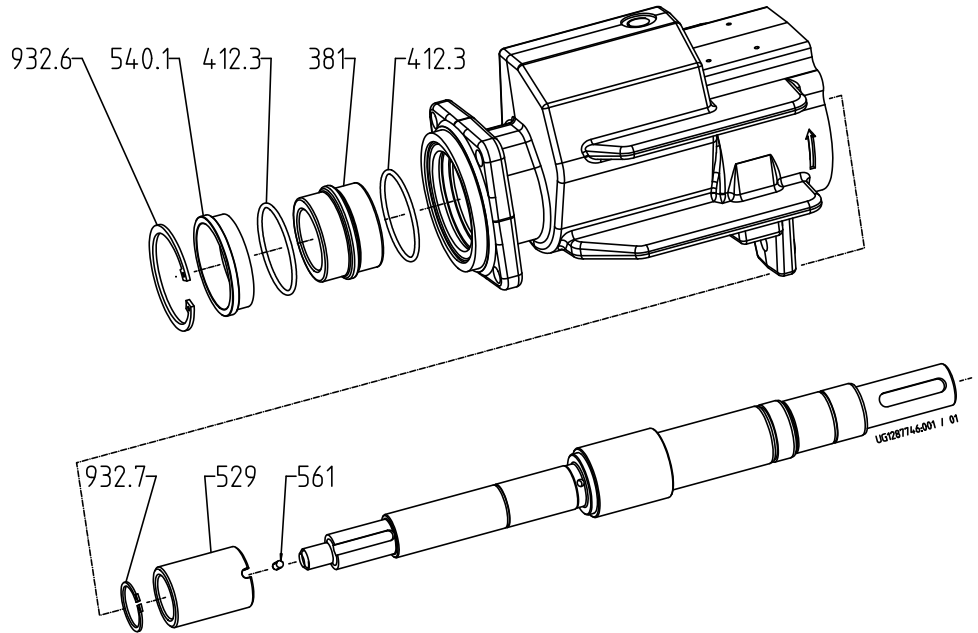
Деталировочный чертеж Etanorm SYT, подшипник скольжения из SiC
